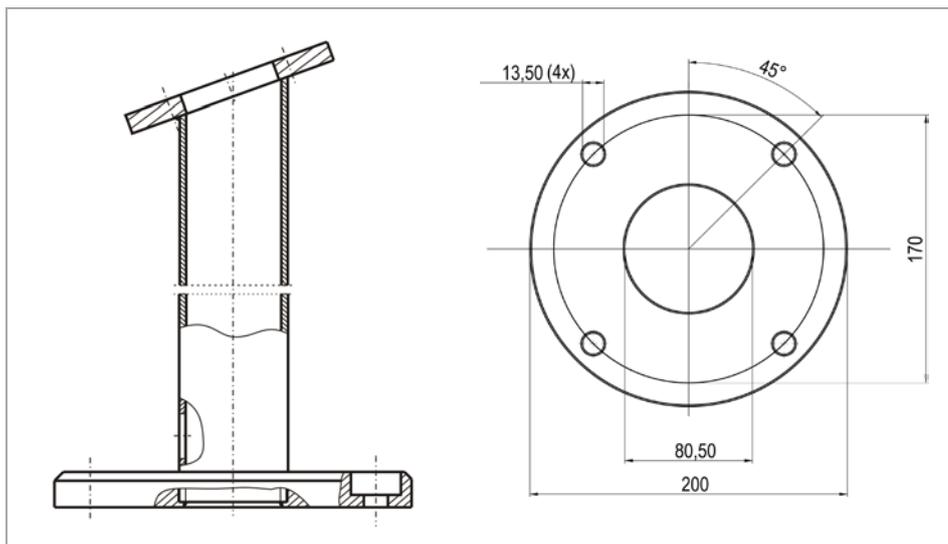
Standfuß - Bohrbild Bodenplatte
